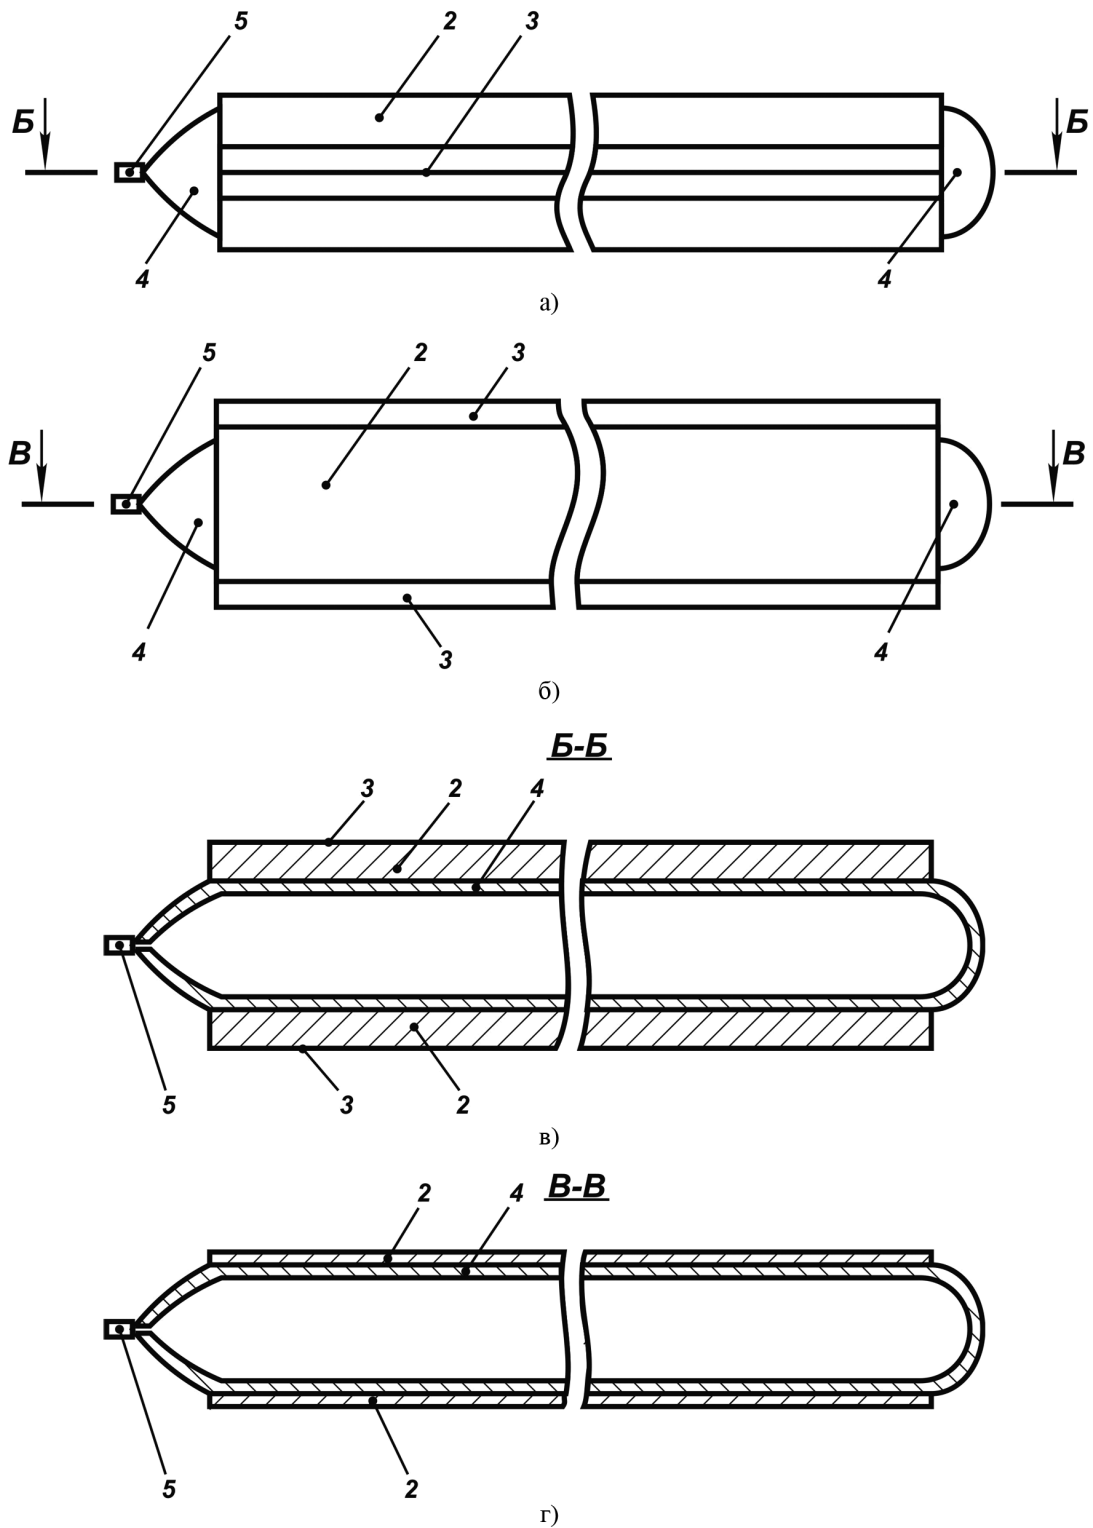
Шина с расположенной внутри пневматической камерой, обеспечивающая соединение плит в колесопровод: а – вид сбоку; б – вид сверху; в – разрез Б-Б; г – разрез В-В
